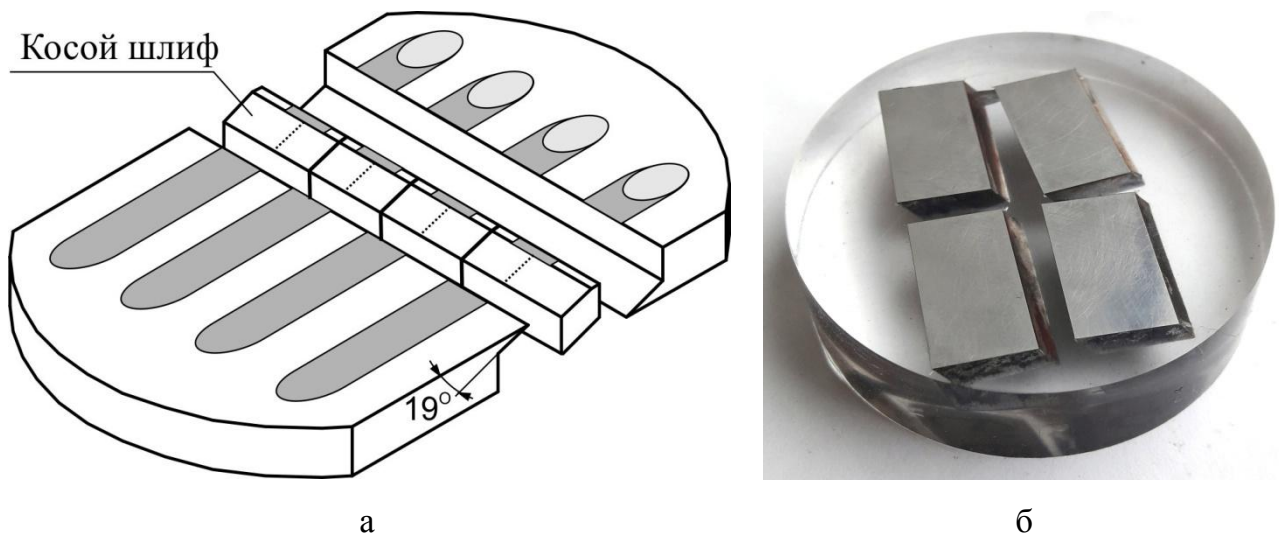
Схема подготовки (а) и фотографии (б) косых шлифов
